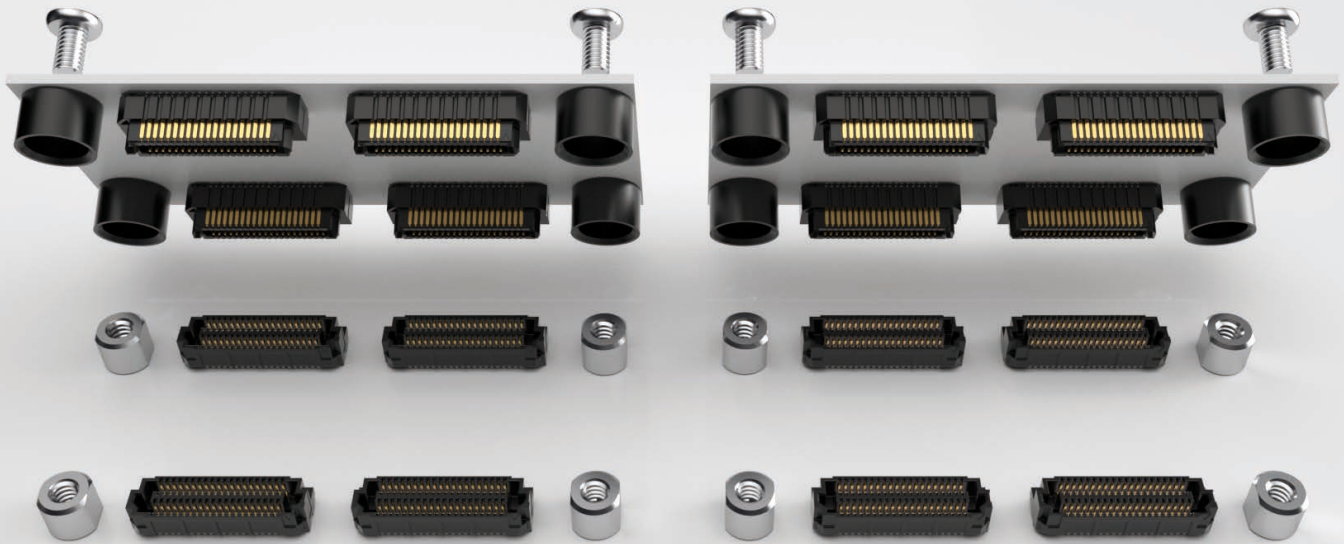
Eine Toleranzstapelanalyse empfiehlt sich für Board-to-Board-Designs mit zwei oder mehr Steckverbindersätzen.
